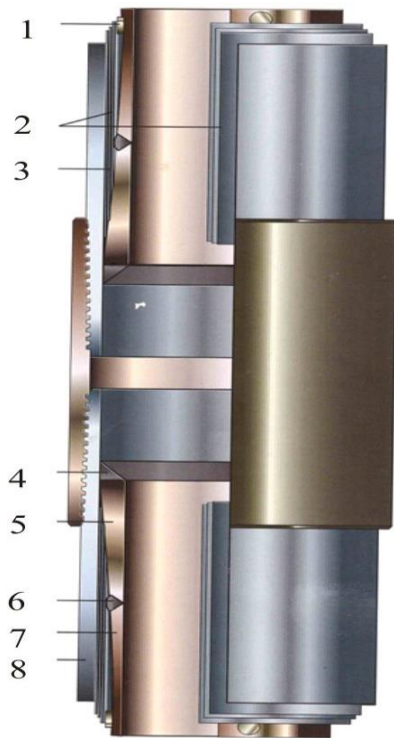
Конструкция направления 711x914 мм [37]
